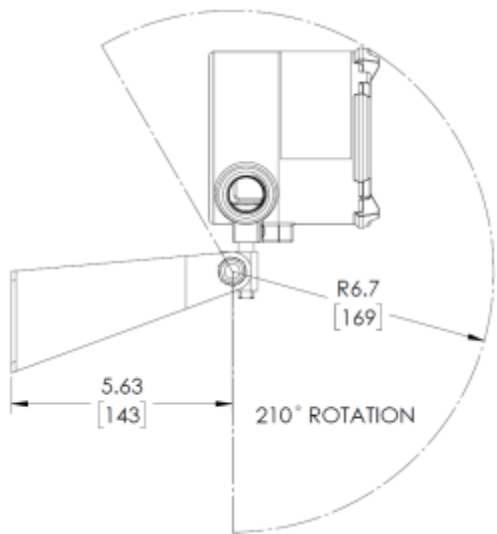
FL500 und Montagebügel, Seitenansicht
